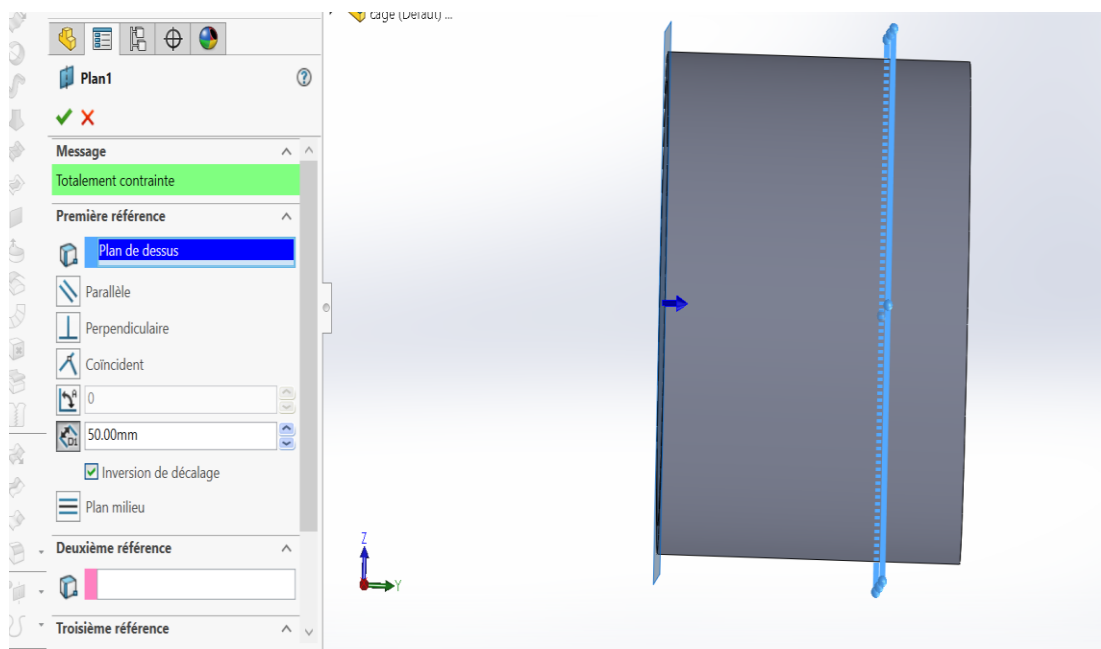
Création d'un nouveau plan parallèle au plan 1
